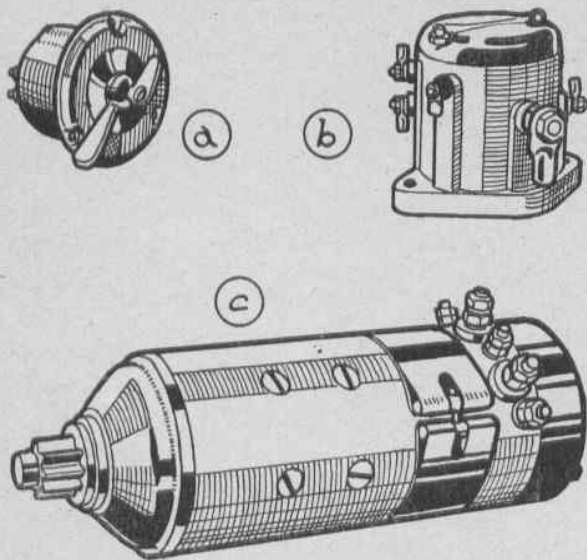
ENSEMBLE DE L'ÉQUIPEMENT DE DÉMARRAGE SCINTILLA.
